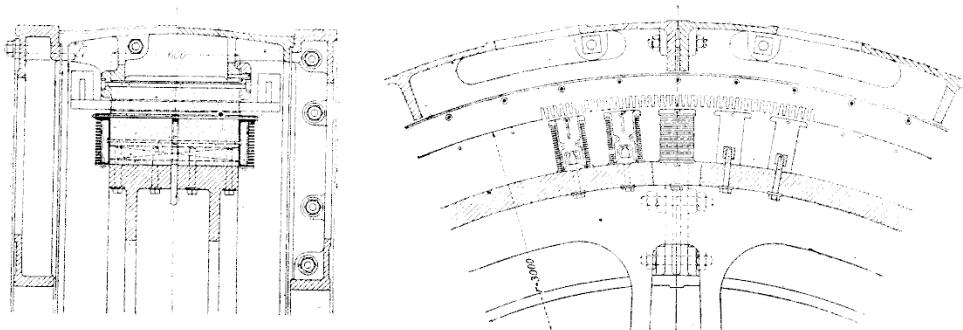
Alternateur triphasé Siemens et Halske. — Détails de construction.
